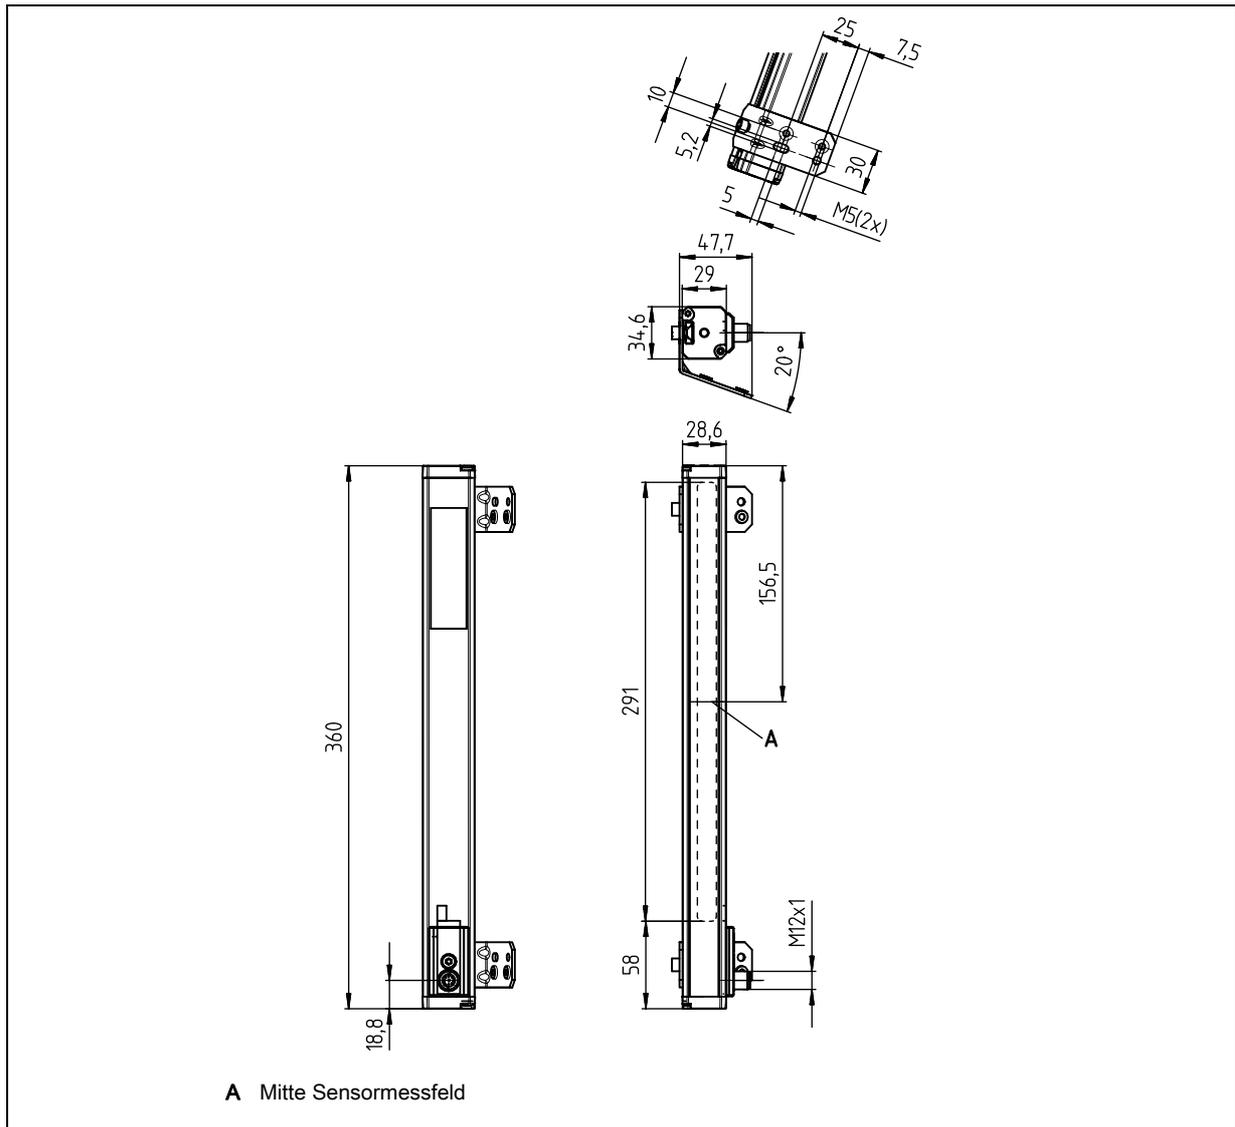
Maßzeichnung OGS 600-280/D...-M12.8 – lange Ausführung
